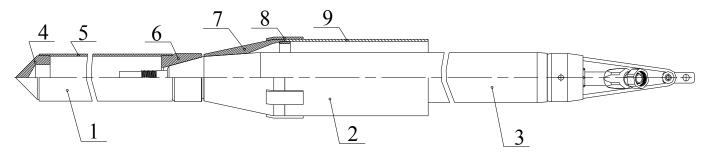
Схема установки удлинителя и расширителя 1- удлинитель; 2- расширитель; 3-пробойник ИП4603A; 4- оголовок; 5- корпус; 6- втулка; 7- головка; 8- планка; 9- корпус.
